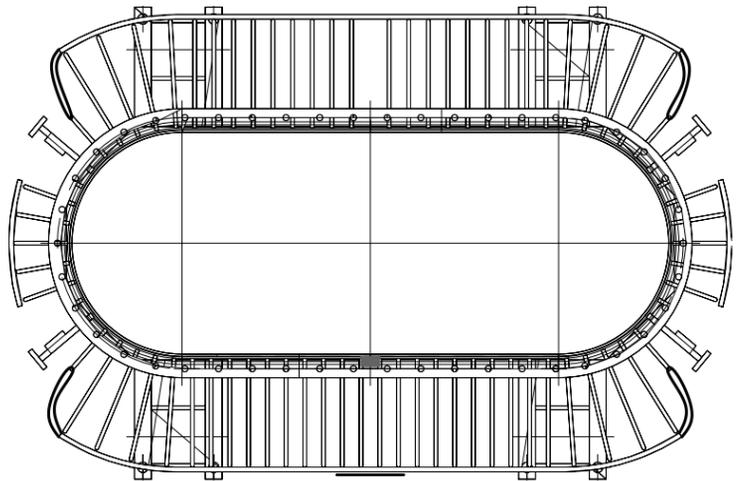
Схема овального бака трансформатора мощностью 630 кВА с одним сварным швом
